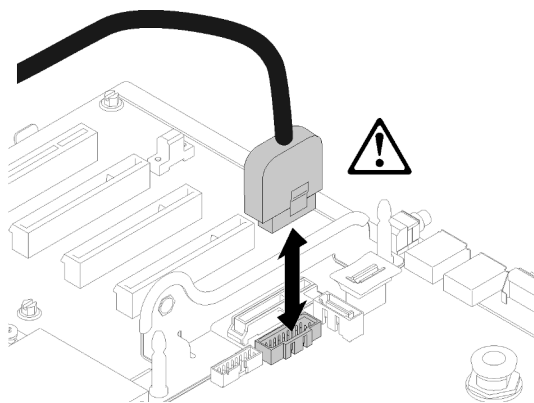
Cable USB 2.0 y cable del panel frontal del operador
